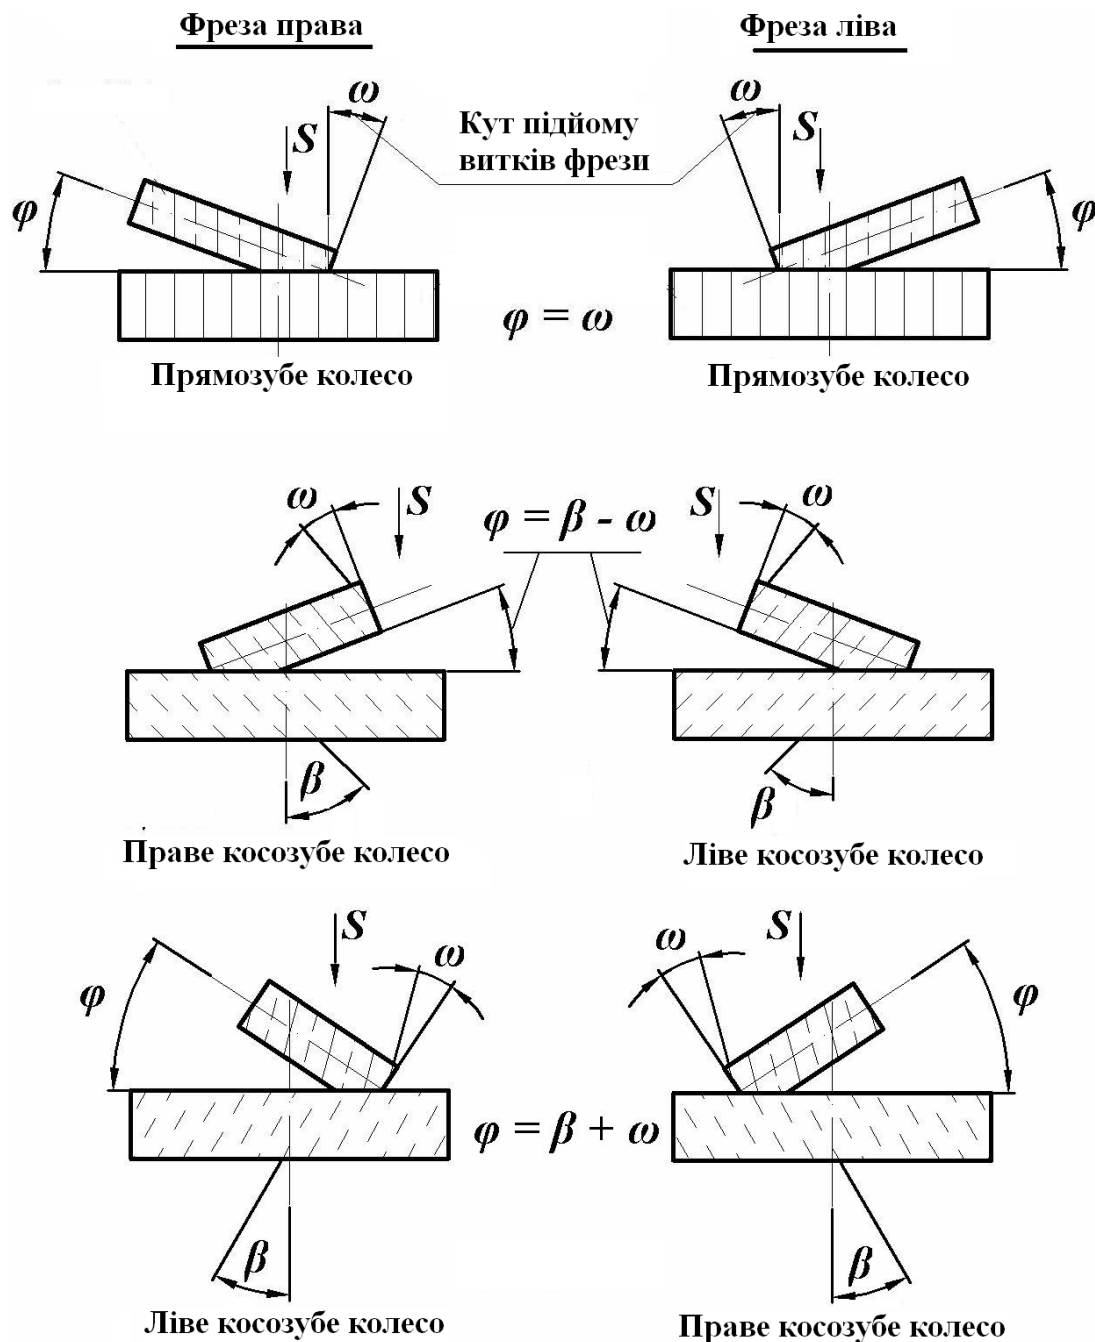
Схеми встановлення фрези при нарізанні циліндричних коліс
